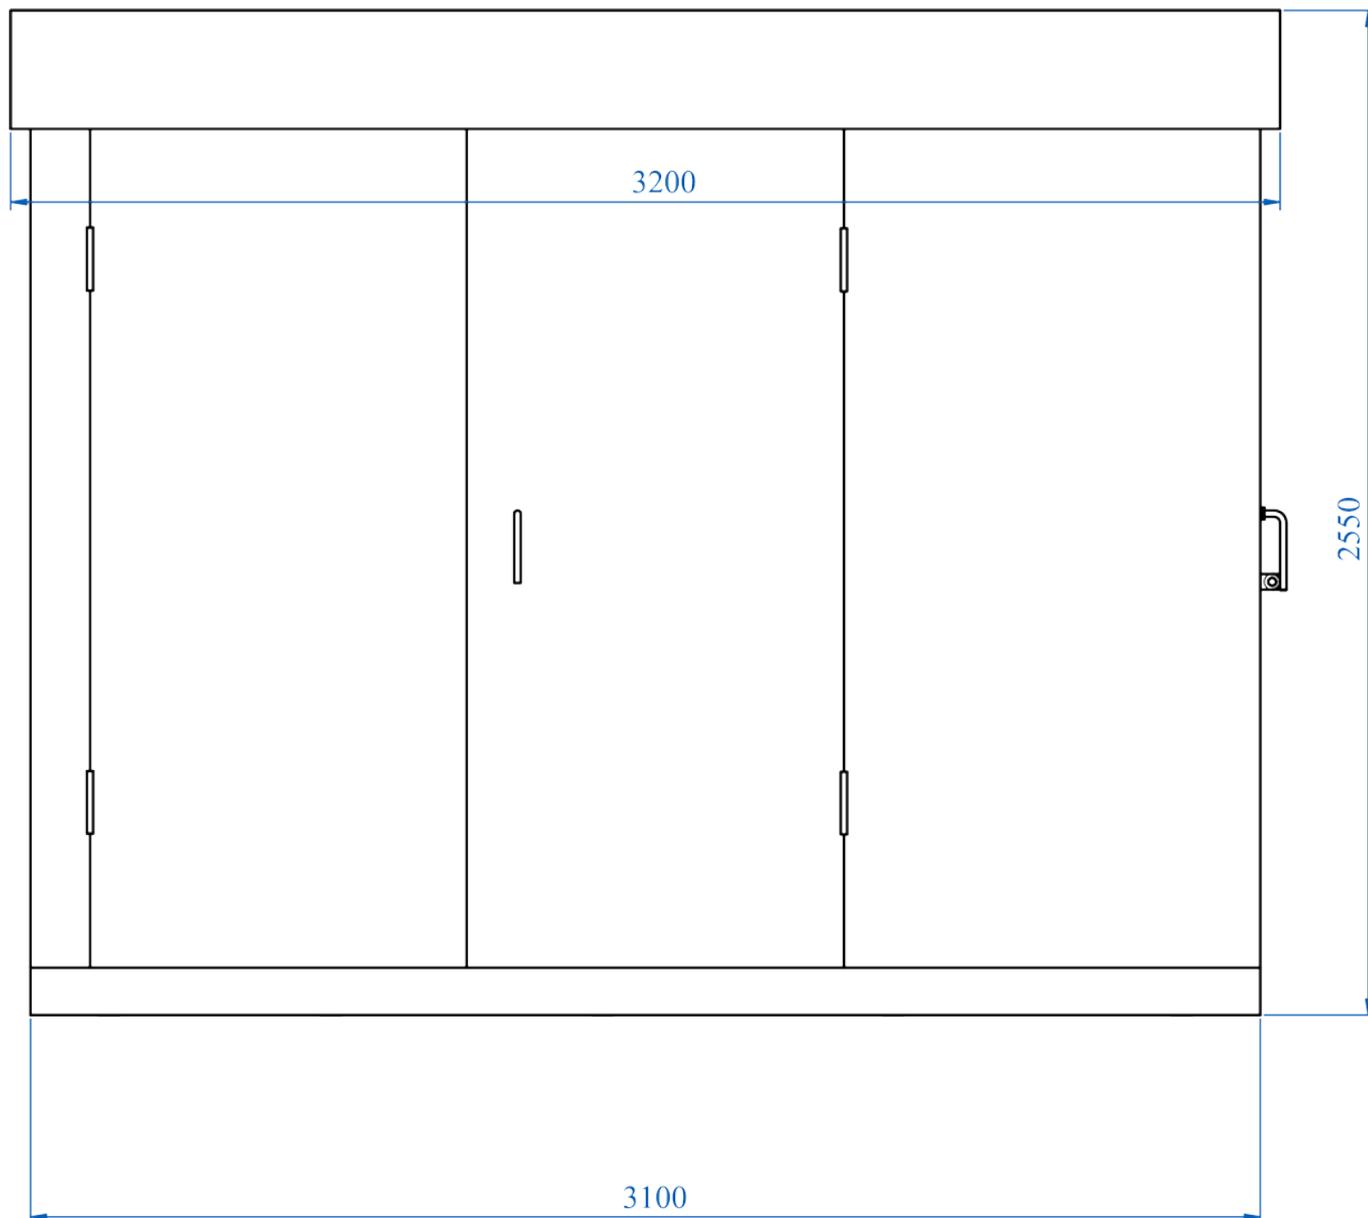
Внешний вид и габаритные размеры КТПН – 250, 400, 630 кВА
